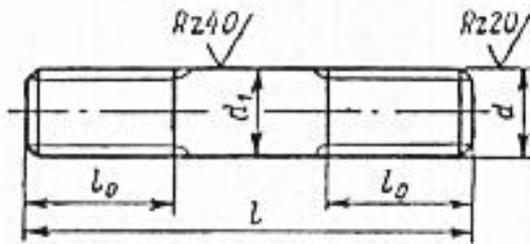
Шпильки повышенной точности для деталей с гладкими отверстиями
